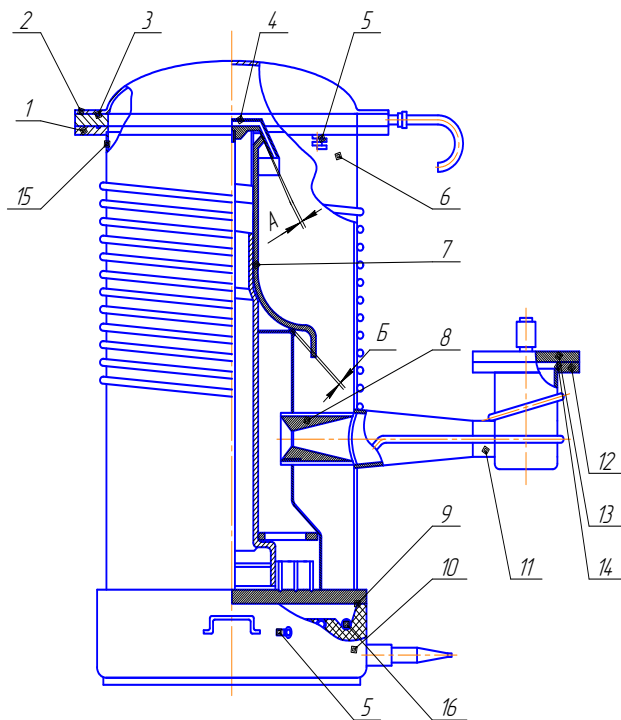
Схема насоса Н-250, Н-400: 1 – фланец входной; 2, 13 – заглушка; 3, 14 – прокладка; 4 – маслоотражатель; 5 – устройство заземления; 6 – корпус; 7 – паропровод; 8 – сопло эжекторное; 9 – дно; 10 – нагреватель; 11 – узел эжекторный; 12 – фланец выходной; 15 – обечайка; 16 – спираль
